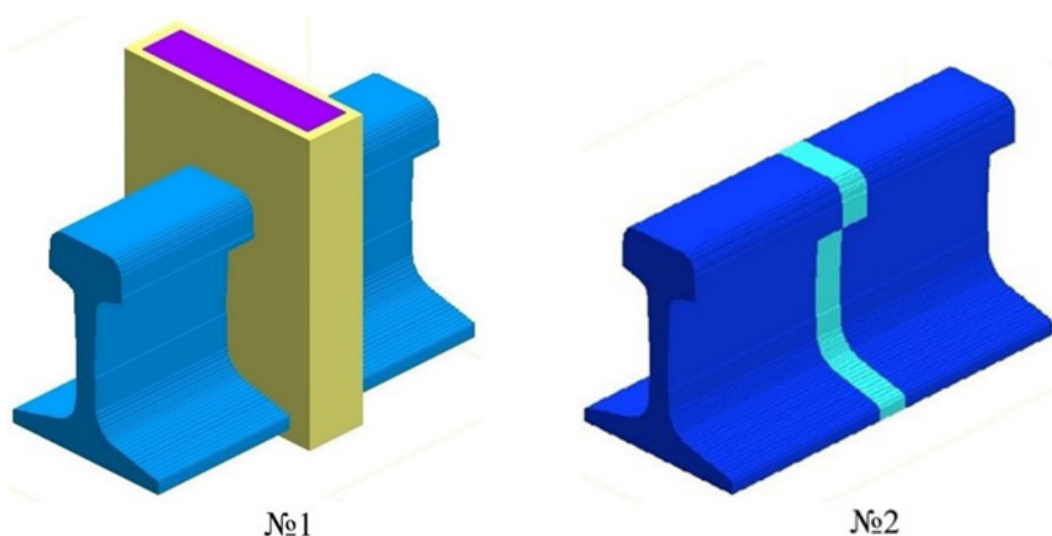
Трехмерные модели термитных сварных соединений рельсов: № 1 – модель сварного соединения с литейной формой, № 2 – модель сварного соединения без литейной формы.
